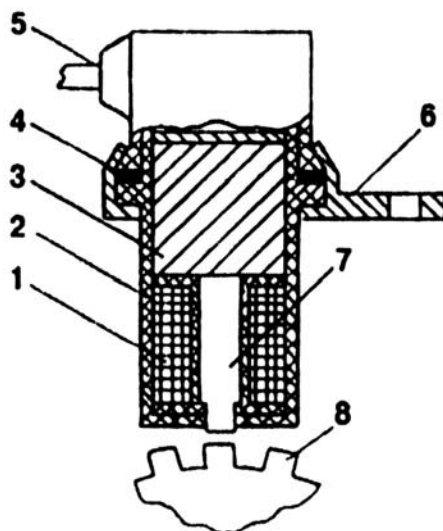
Датчик положения коленчатого вала: 1 - катушка датчика; 2 - корпус; 3 - магнит; 4 - уплотнитель; 5 - привод; 6 - кронштейн крепления; 7 - магнитопровод; 8 - диск синхронизации
